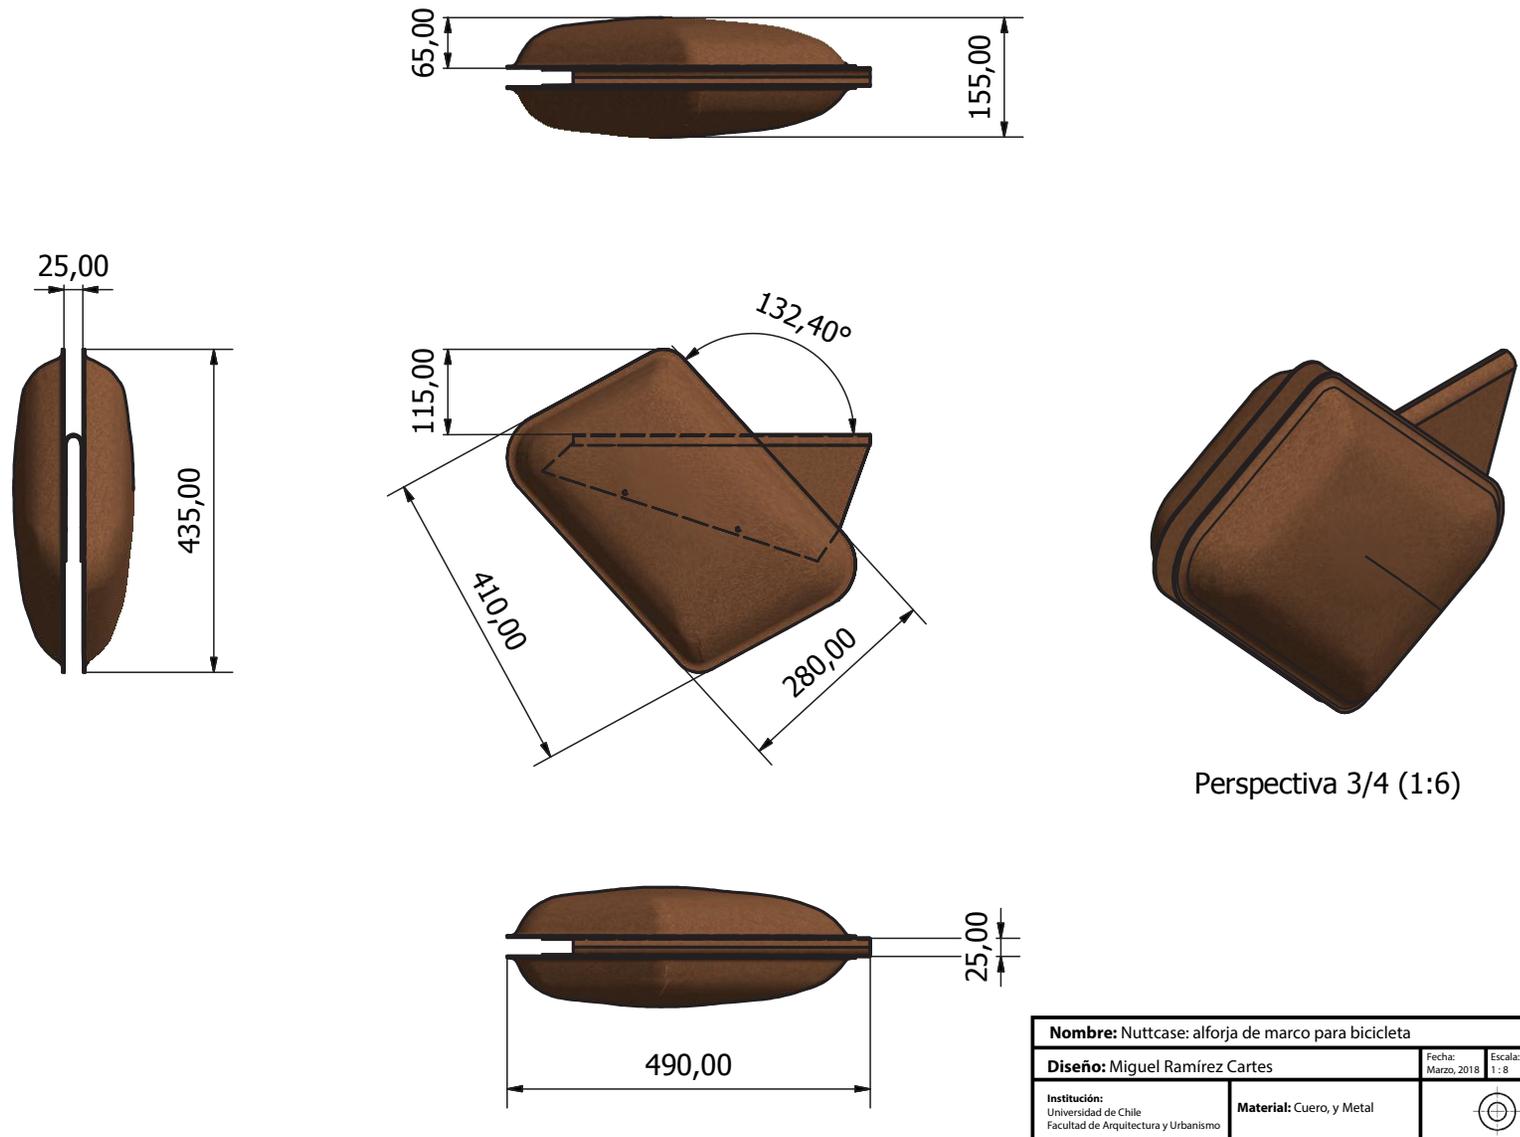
Planimetría general propuesta final. Elaborado por autor.
